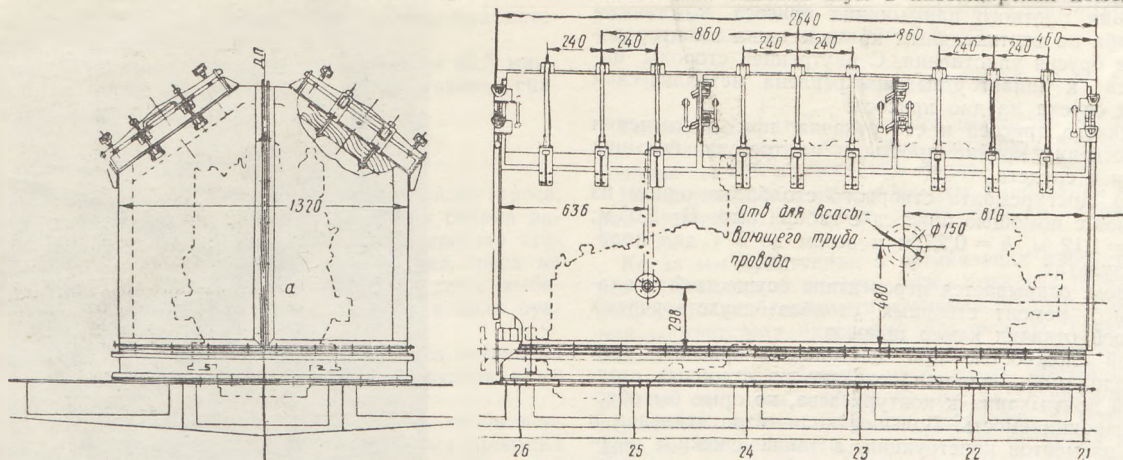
Общий вид звукоизолирующего кожуха для двигателя ЗД6
